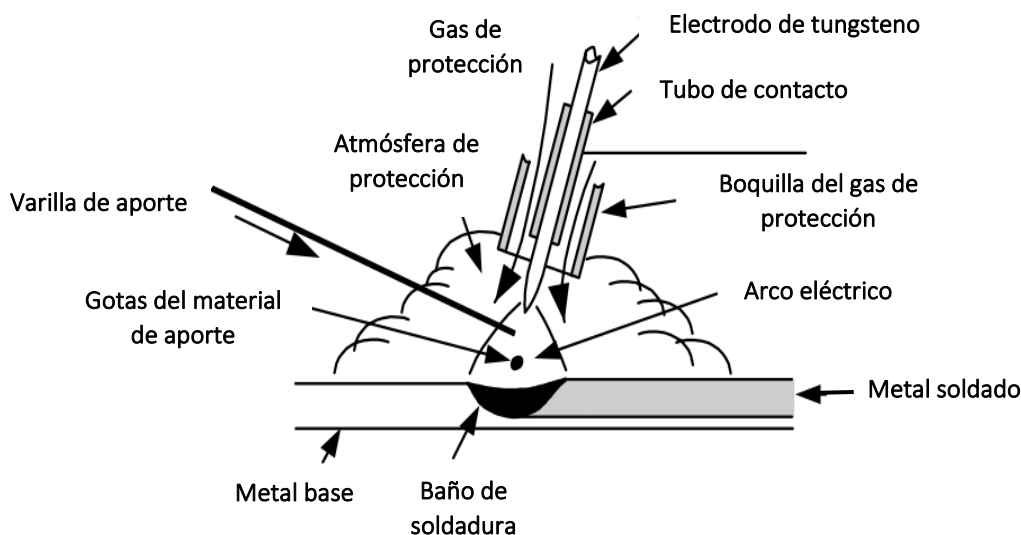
Proceso de soldadura GTAW (Por sus siglas en inglés “*Gas tungsten arc welding*”) [7].
